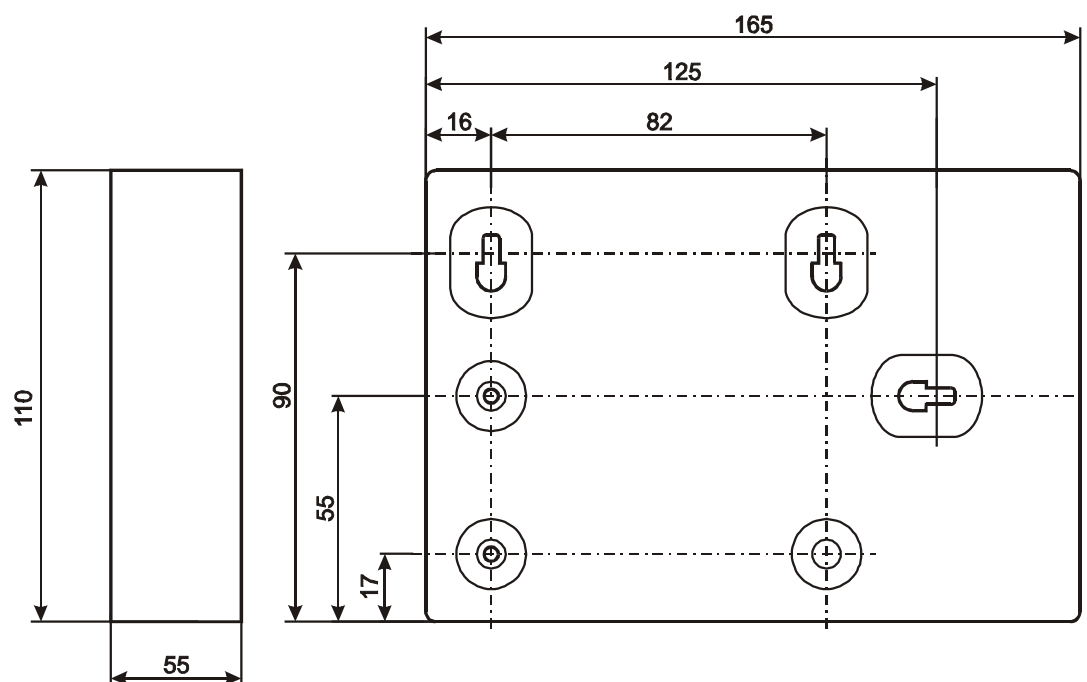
Внешний вид и габаритные размеры БРА-03-4 в исп. IP20
